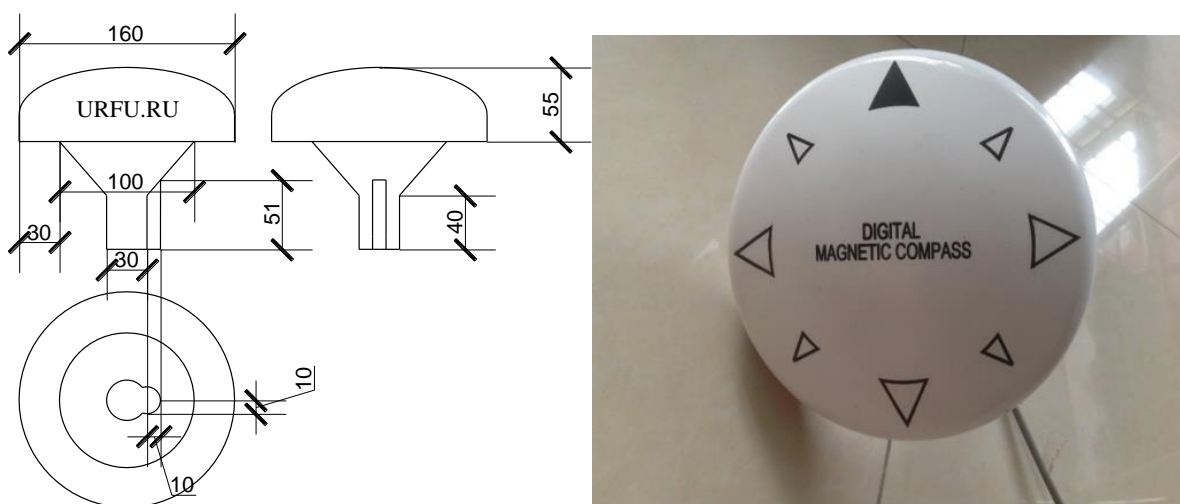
Устройство цифрового магнитного компаса после изготовления
